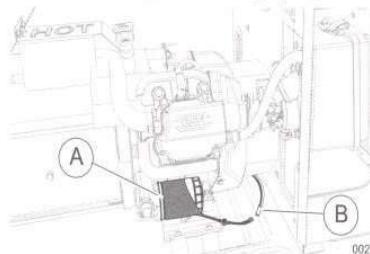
Установка обогревателя масляного фильтра (9 кВт)
